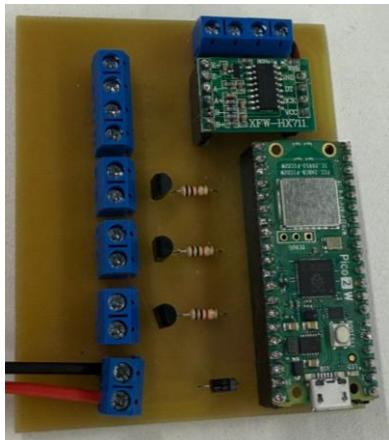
Vista superior da PCB com Pico 2W, HX711 e transistores.
